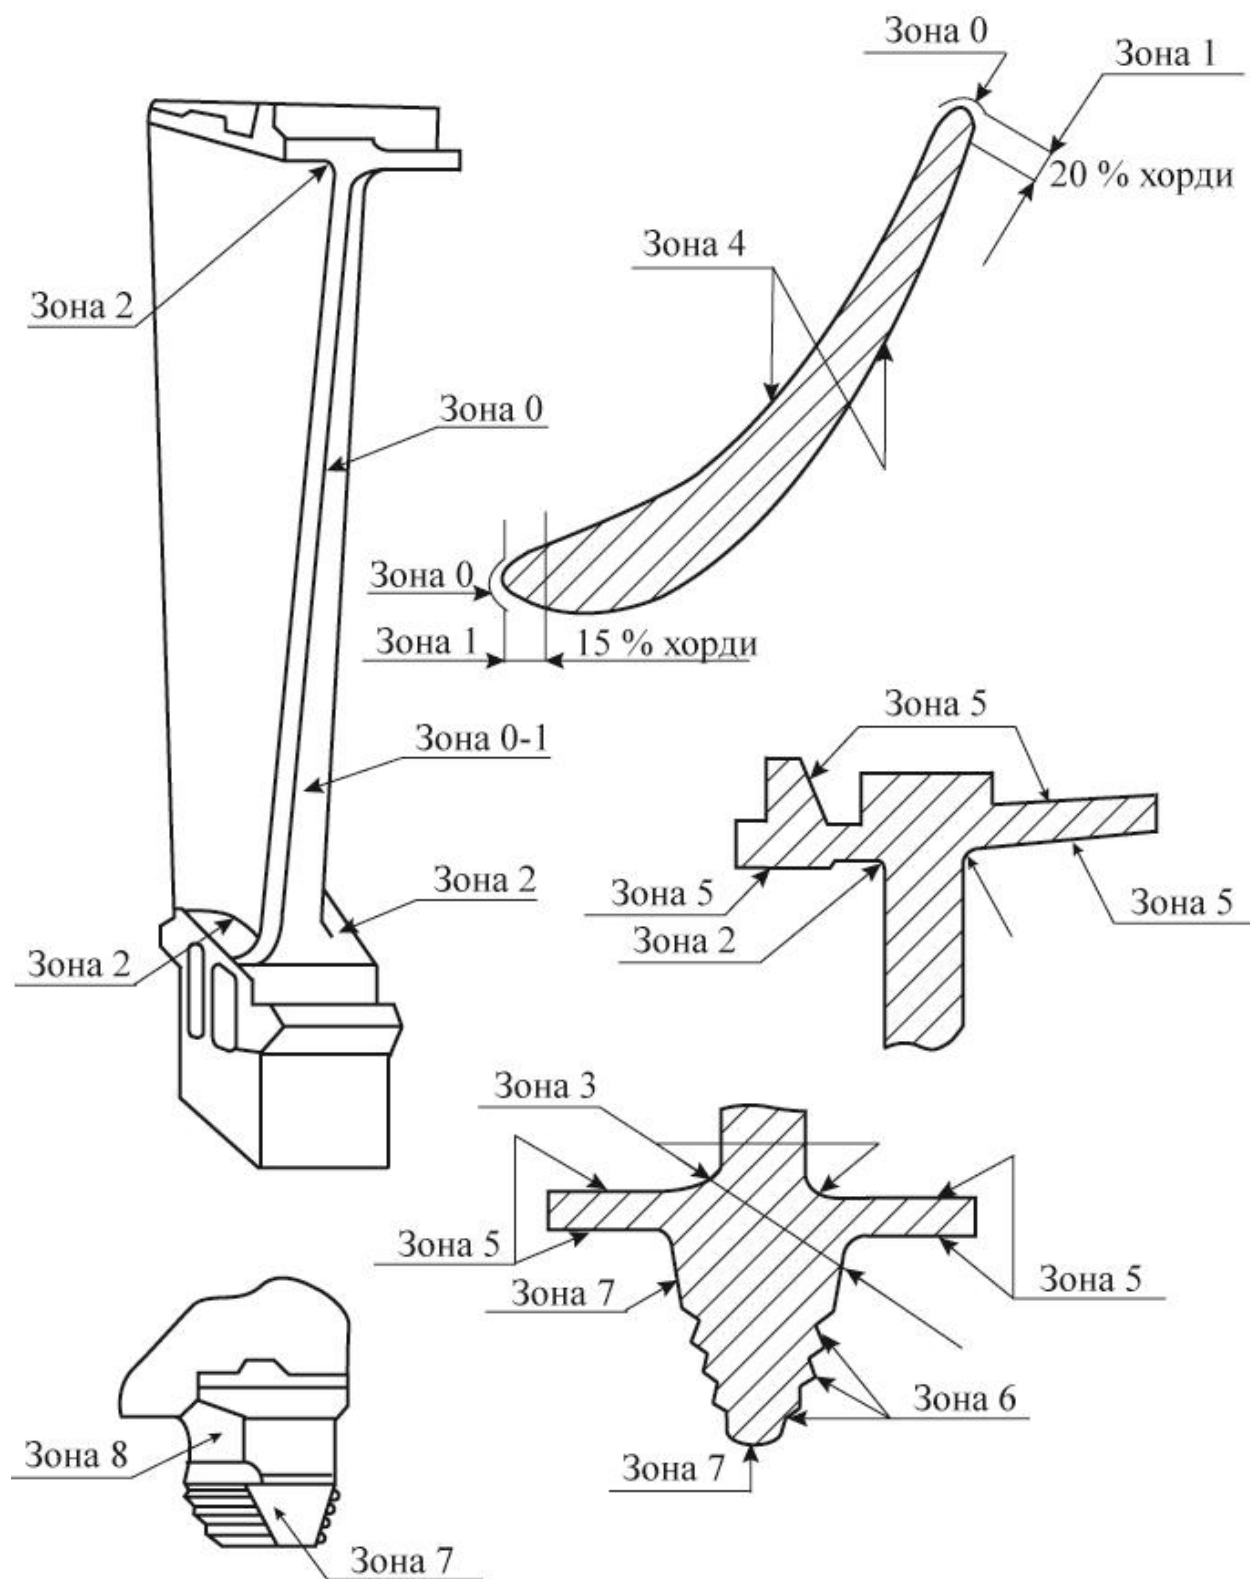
Схема робочої неохолоджуваної лопатки
